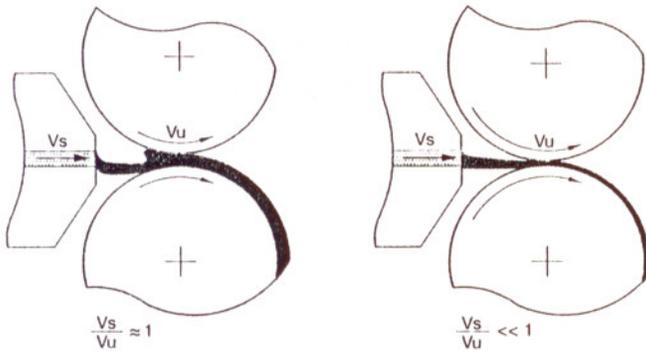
Zustände beim Herausziehen einer Schmelze aus einem horizontal angeordneten Werkzeug
